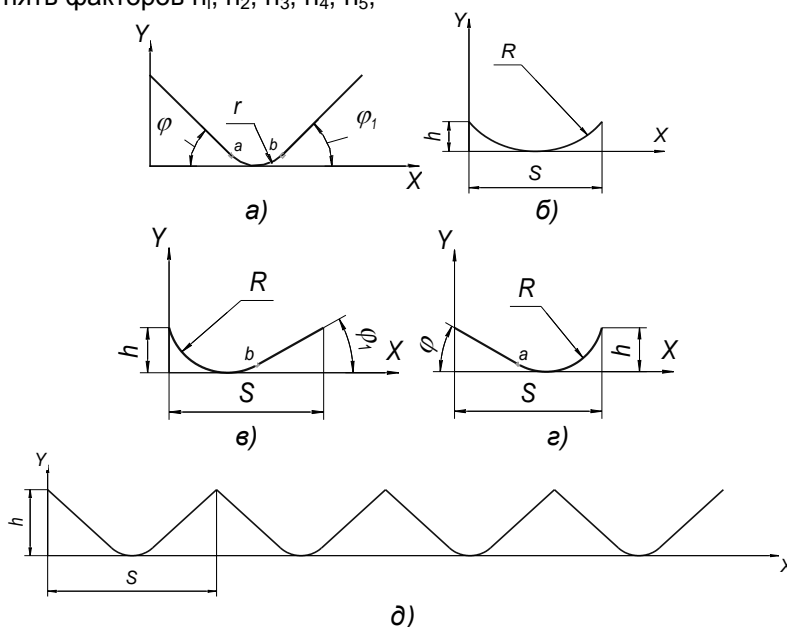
Расчет профиля обработанной поверхности копированием профиля инструмента: а) риска с двумя линейными и радиусным участками; б) риска, содержащая только радиусный участок; в, г) риска, содержащая радиусный и линейный участки; д) полный профиль обработанной поверхности
